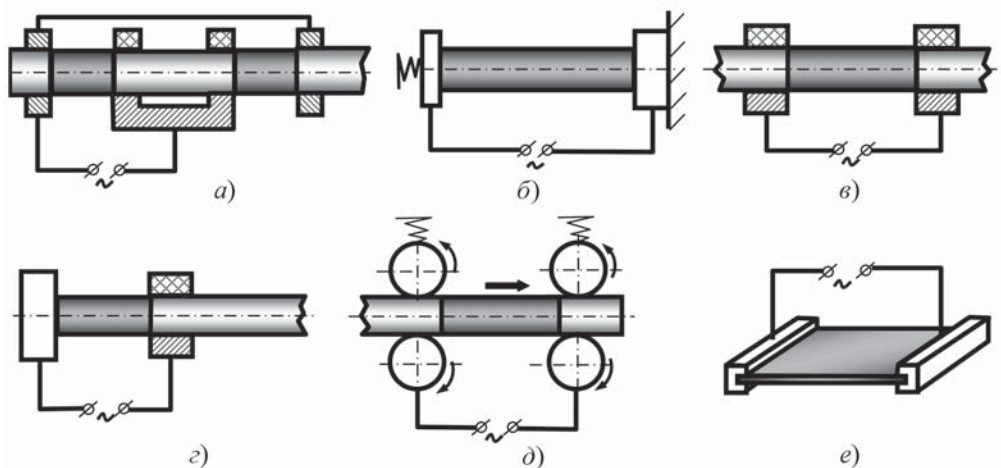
Некоторые схемы электроконтактного нагрева заготовок:
